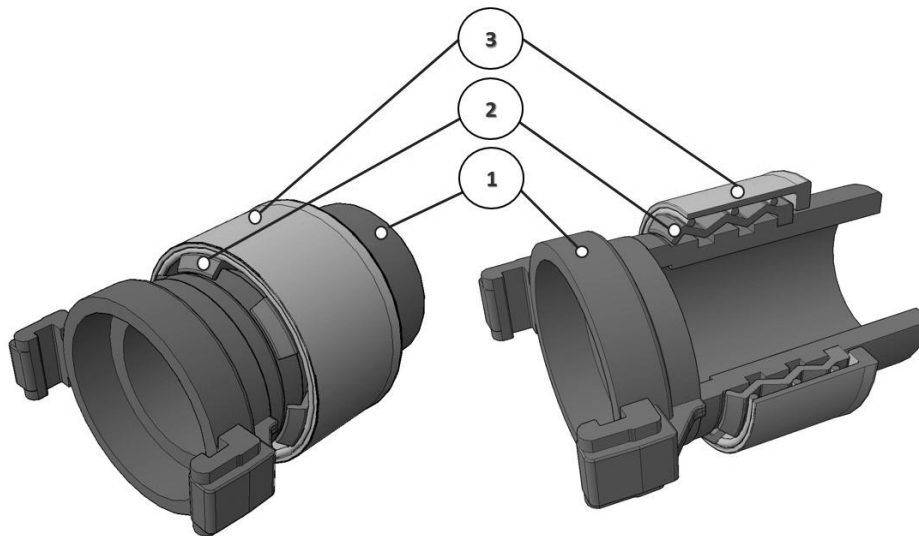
Модель устройства для крепления пожарного рукава к соединительной головке
